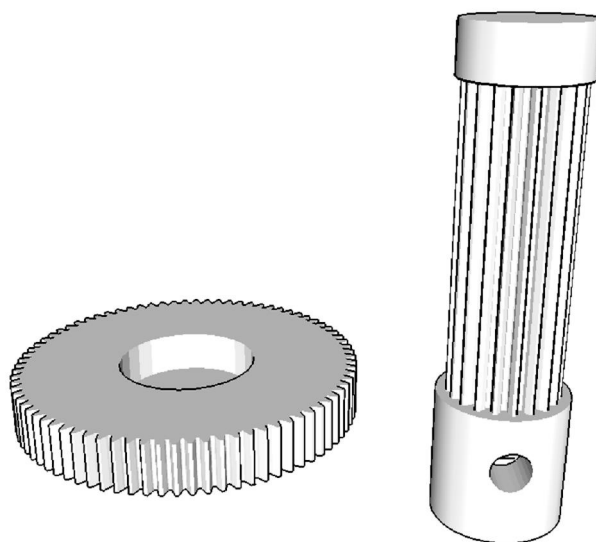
Desenho 3D das engrenagens. À esquerda está a engrenagem do micrômetro e, à direita, a engrenagem do motor.
